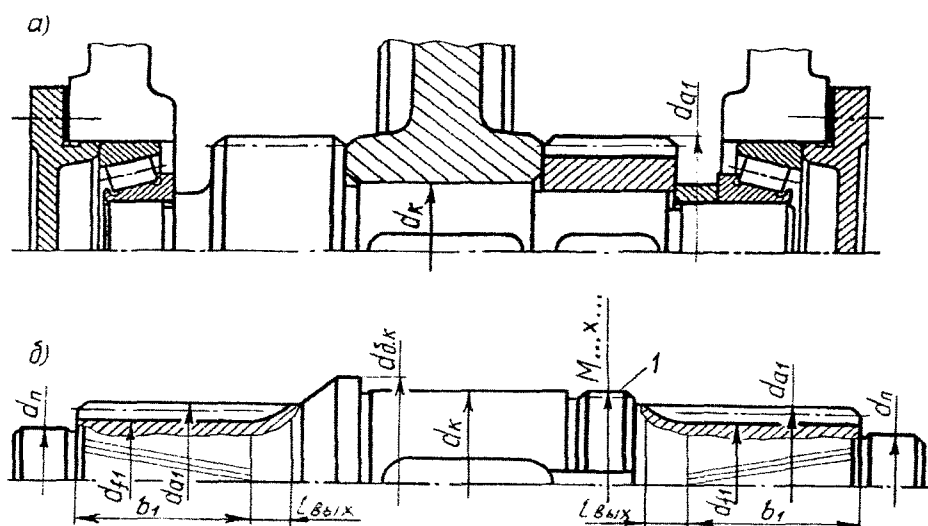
Примеры конструкций промежуточного вала редуктора с раздвоенной тихоходной ступенью (вал II на схеме рис. 3.3, е)
